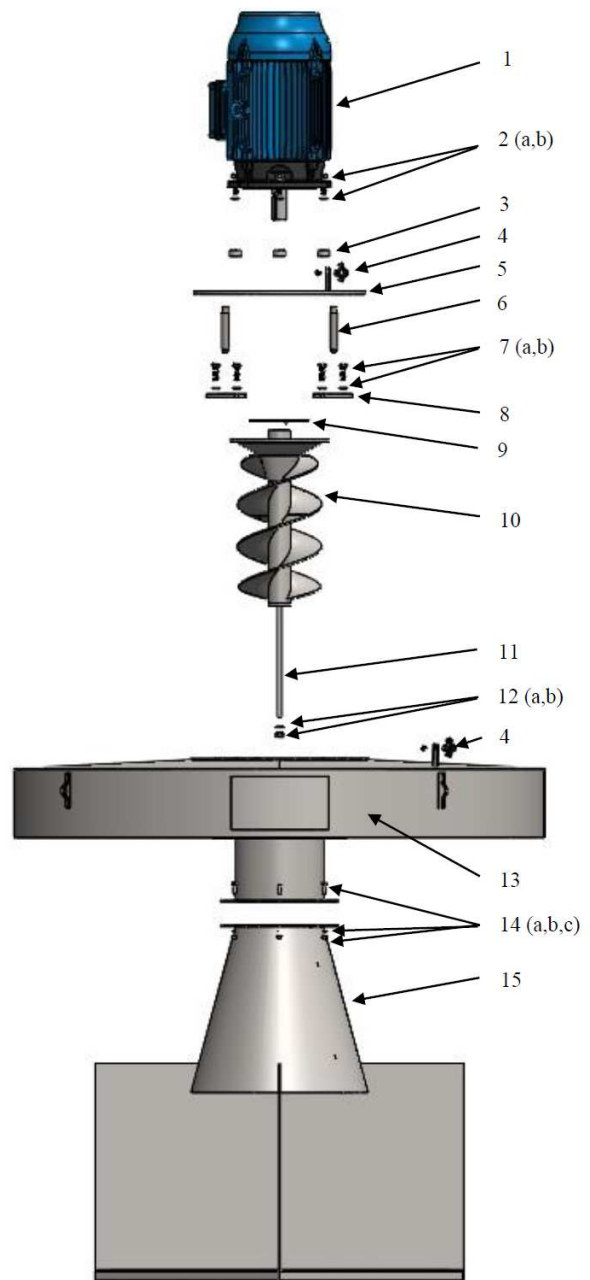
Explosionszeichnung des ATB - HSA mit Stabilisierungskreuz
